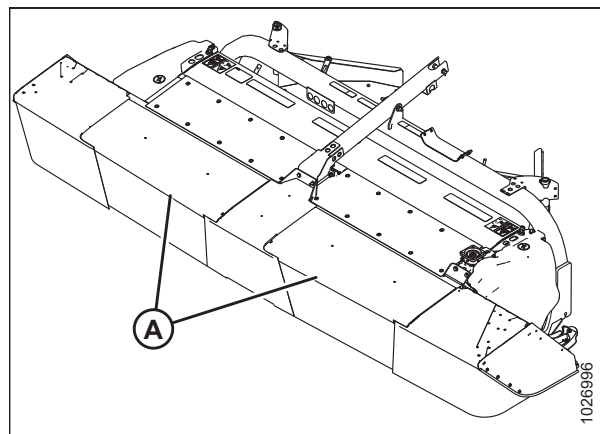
Щитки и шторы ножевого бруса – Жатка
